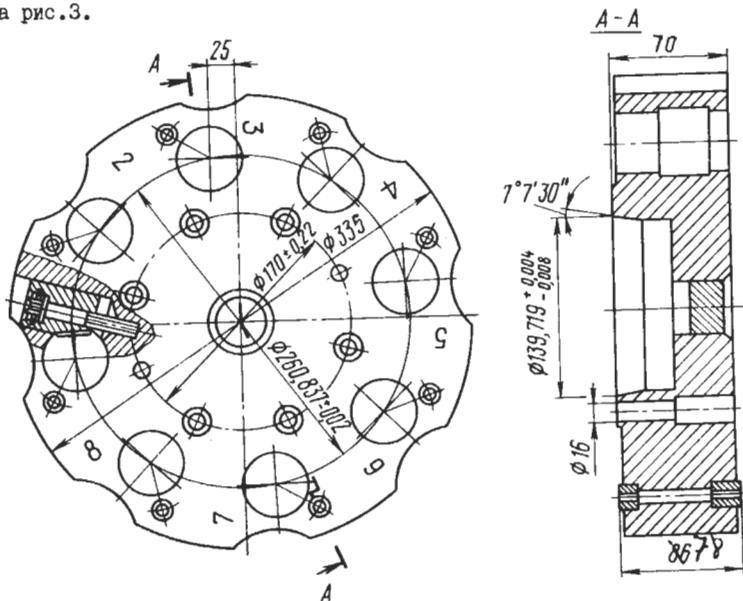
Инструментальный диск восьмипозиционный УГ9326.0300.000
